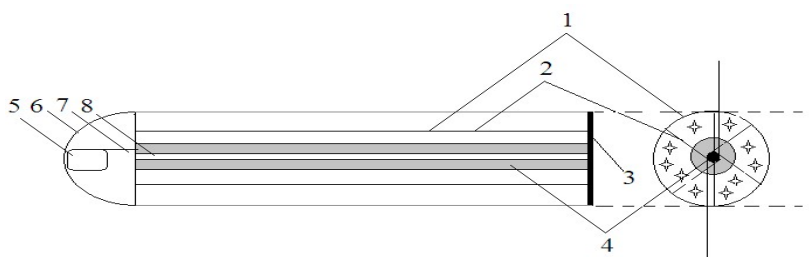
Модель контейнеру з порошковою вогнегасною речовиною: 1 – корпус; 2 – розділювач секцій; 3 – задня торцева частина контейнеру; 4 – спонукальний пристрій; 5 – механізм приведення в дію спонукального пристрою; 6 – лобова частина; 7 – запальник механізму; 8 – центральна вісь
